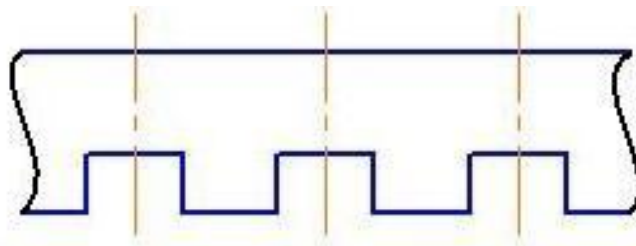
елемент хордової насадки зі спеціальними вирізами.
